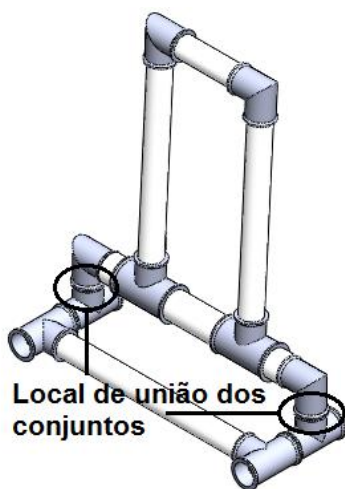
Montagem dos módulos – Módulo 4 – Passo 8
